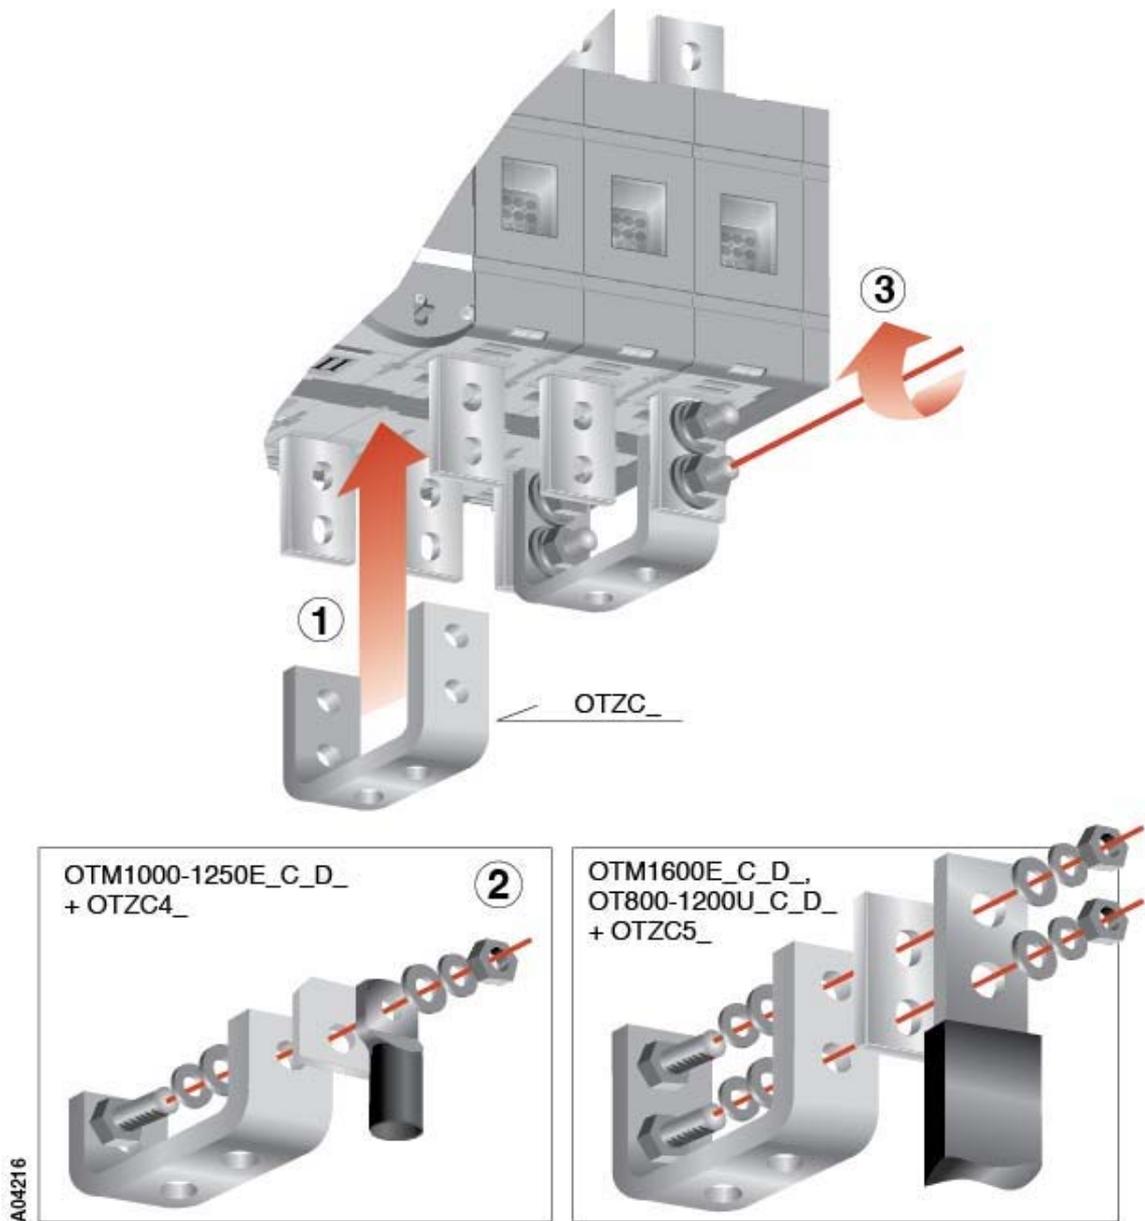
Установка соединительных шин (тип OTZC_) на автоматические реверсивные выключатели нагрузки OTM1000...1600_C_D_ и OTM800...1200U_C_D
